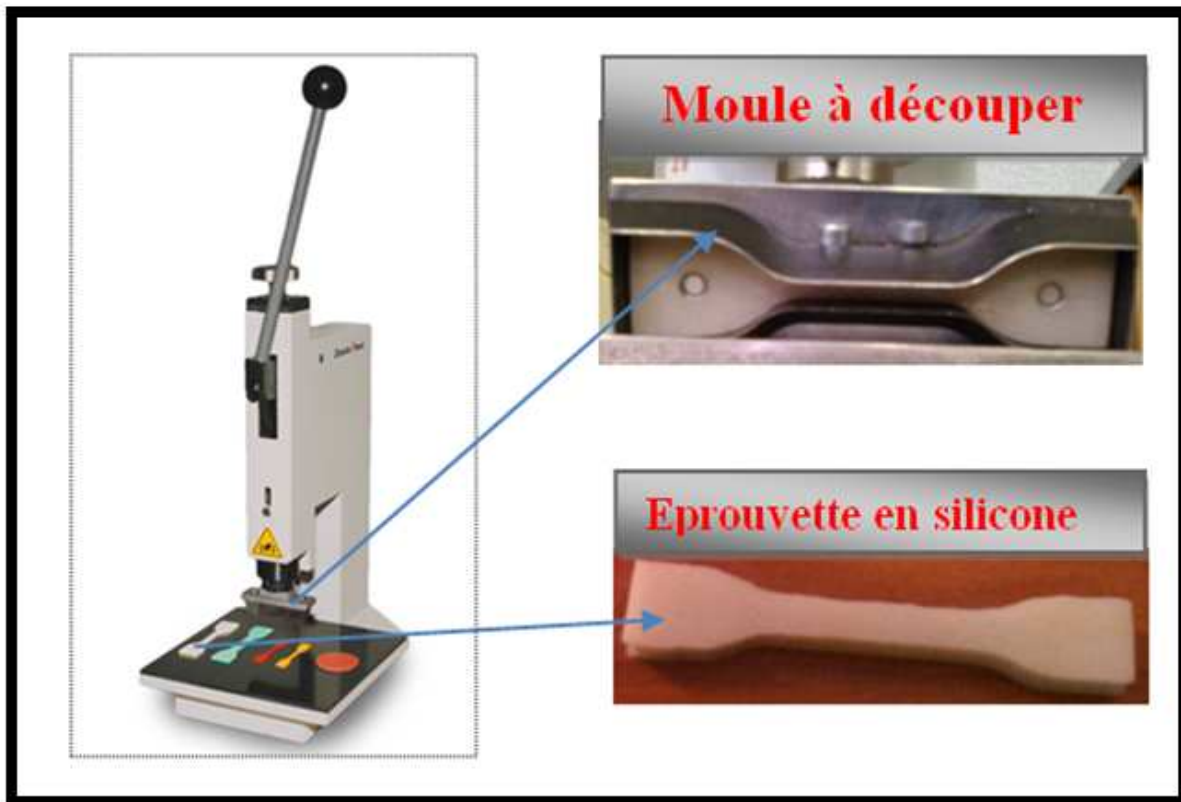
Presse manuelle Zwick 7101 coupe éprouvette.
